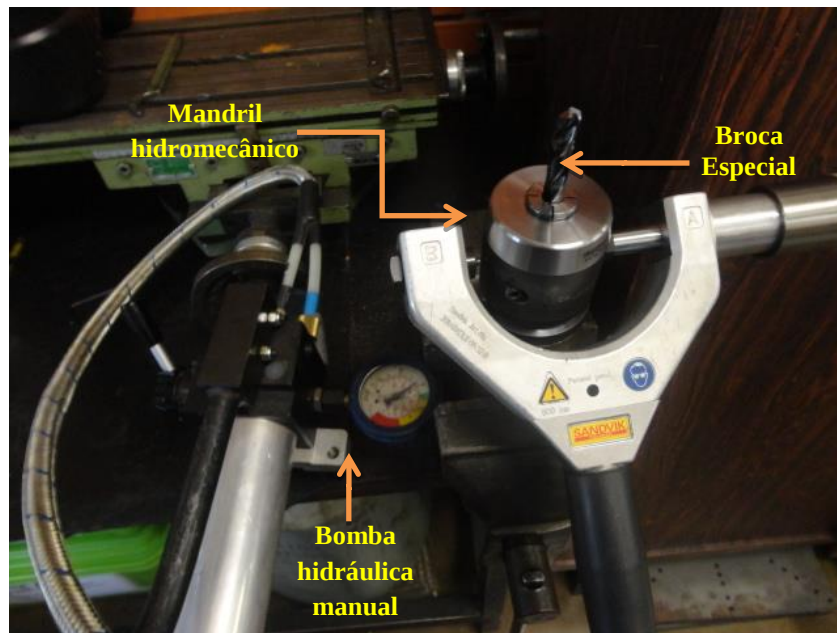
Sistema de fixação das ferramentas para o processo de usinagem com mandril hidromecânico.
